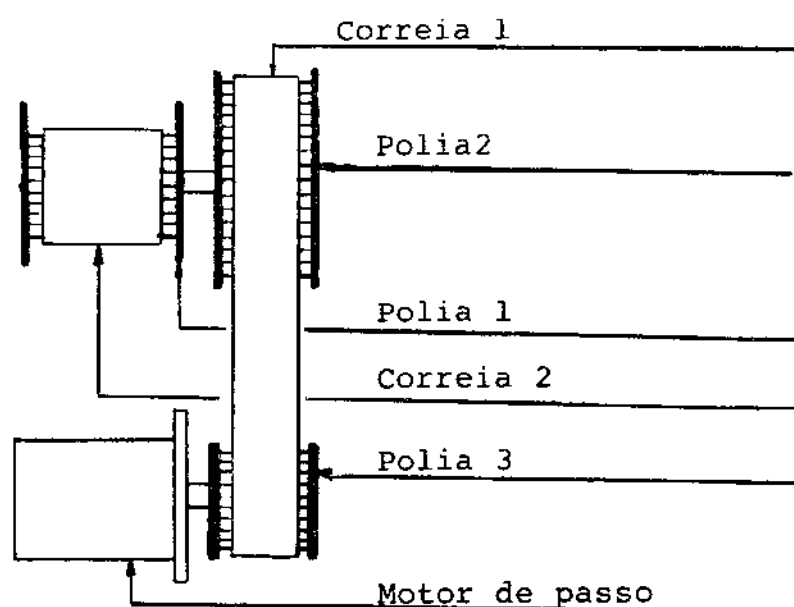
b- Vista lateral do conjunto de polias e motor de passo do acionador mecânico.
